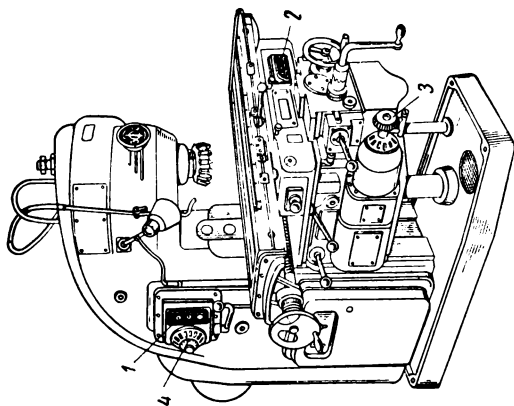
Расположение кнопочных павелей на фрезерном станке
